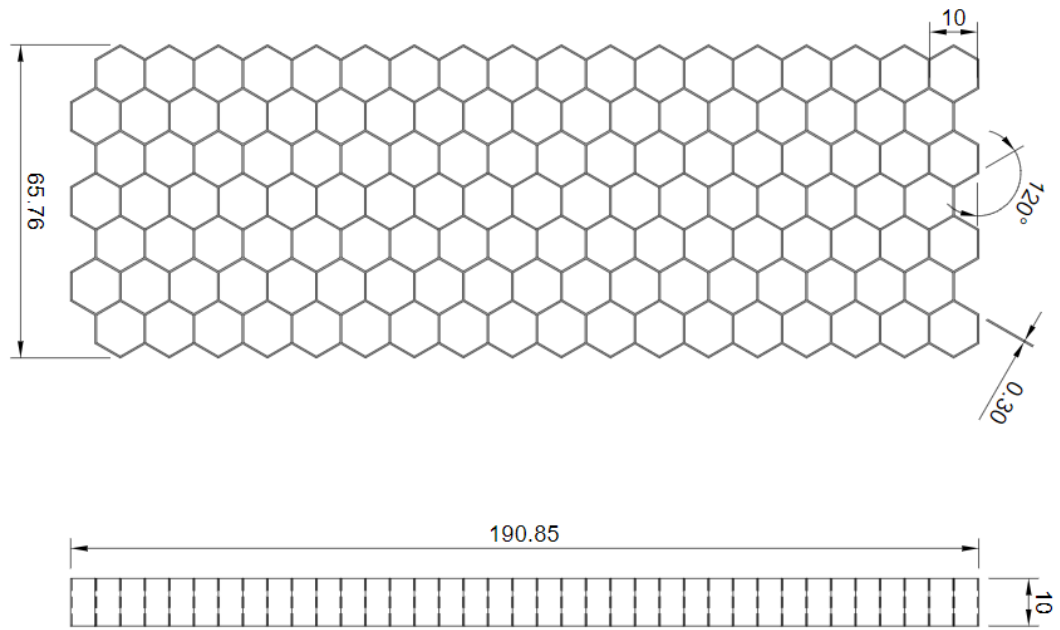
Dimensões honeycomb hexagonal – Fonte: (Autor)
